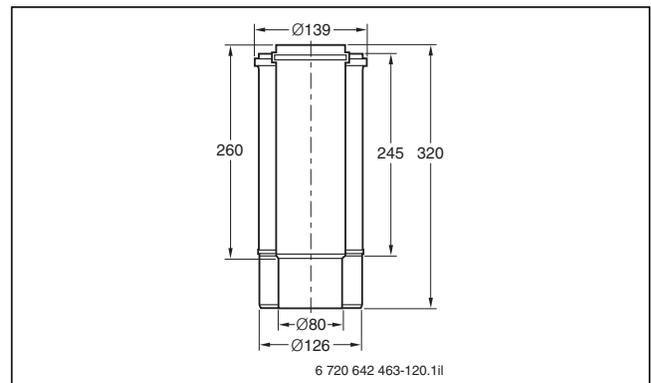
Konzentrisches Schiebestück DN 80/125 (Maße in mm)
